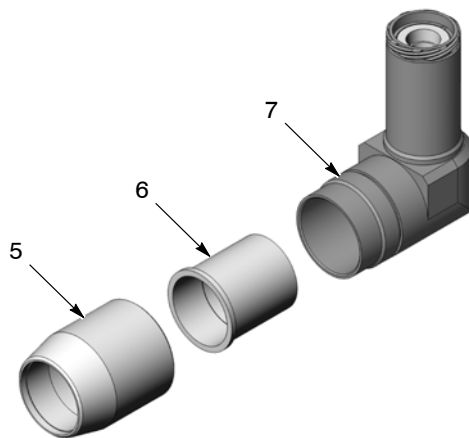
Демонтаж гайки корпуса и крепежной гайки
